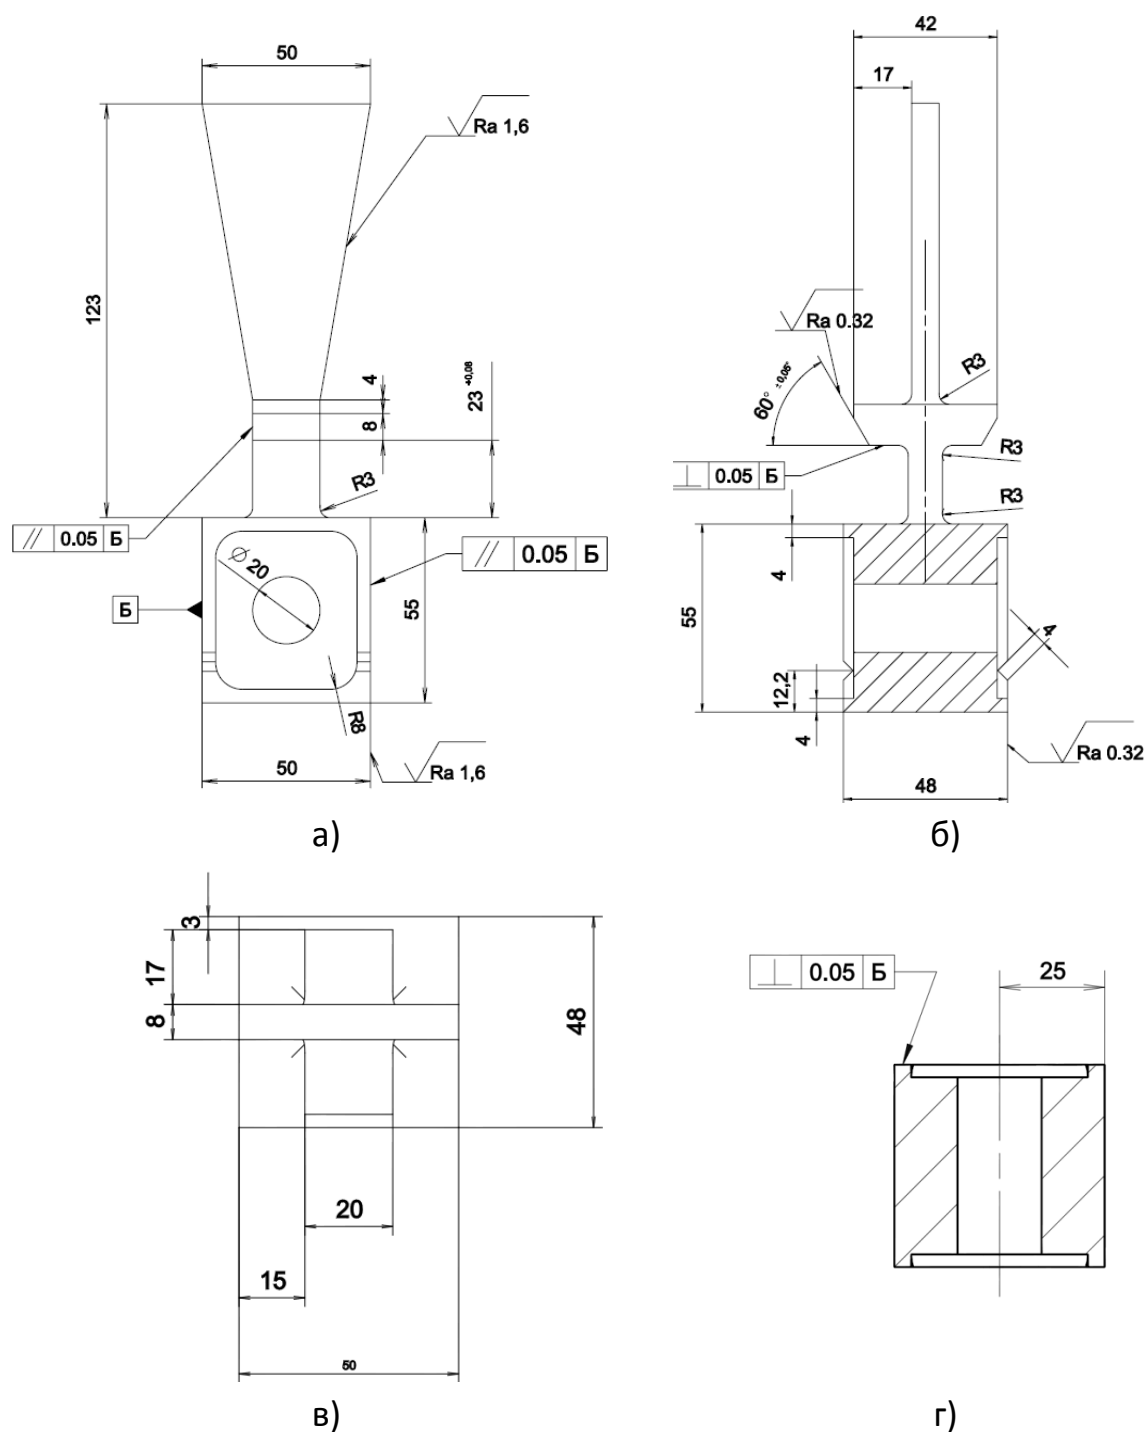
Эскиз исследуемой лопатки-имитатора: а) фронтальный вид; б) боковой вид; в) вид сверху; г) вид с разрезом соединительного отверстия.
